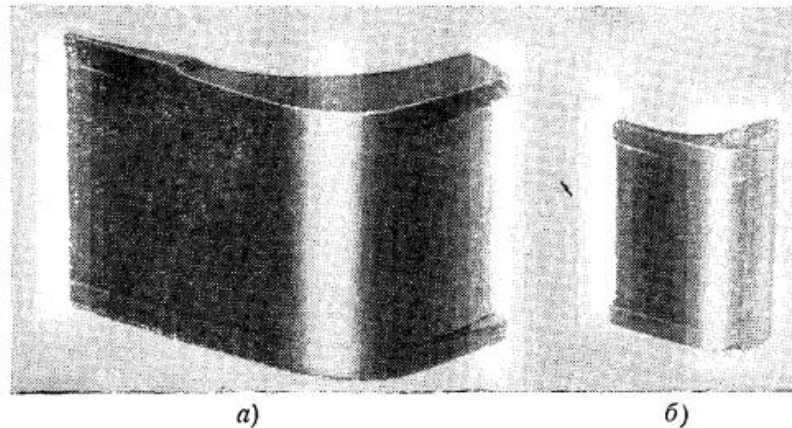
Направляющие лопатки сварных диафрагм [1]:
